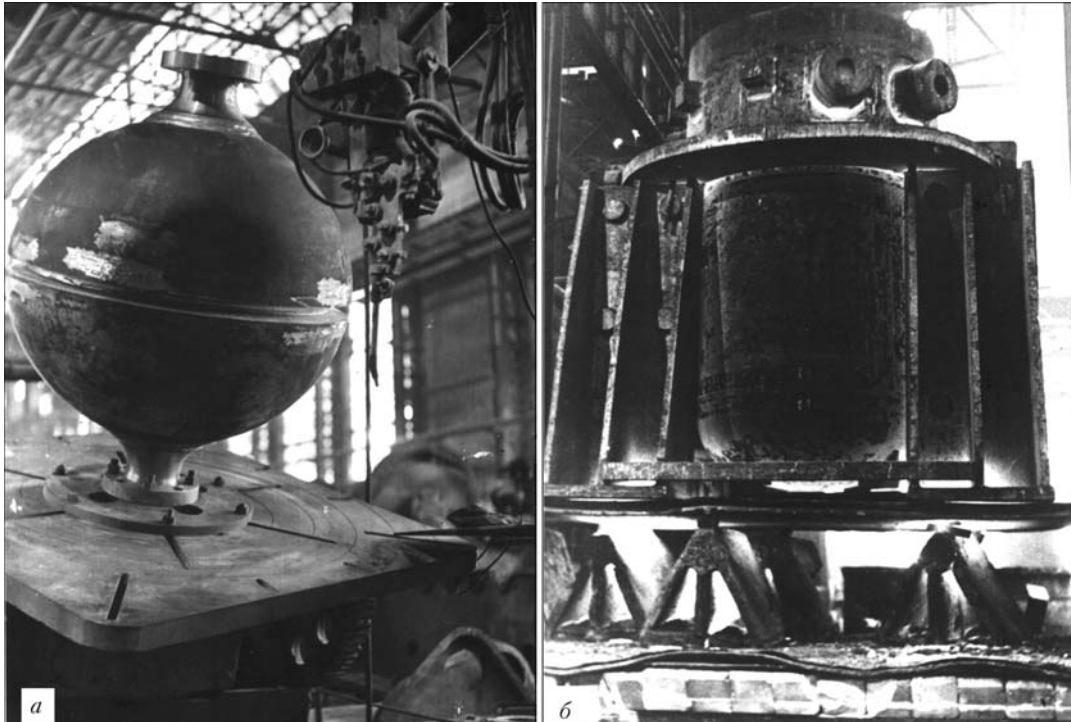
Патрубки, сваренные автоматической сваркой под флюсом с корпусом шарообразного сосуда высокого давления (а) и штамповарной корпус с приваренными методом ЭШС патрубками (б) в стенде на подине печи после нормализации
